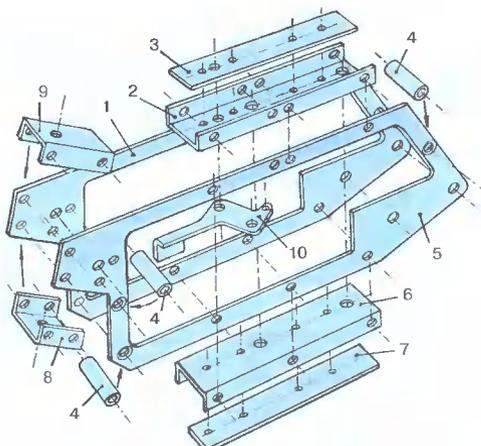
Детали рамы: 1 — правая боковина; 2 — верхняя деталь рамы; 3 — верхняя опорная планка; 4 — распорная втулка; 5 — левая боковина; 6 — нижняя деталь рамы; 7 — нижняя опорная планка; 8 — нижний кронштейн оси поворота; 9 — верхний кронштейн оси поворота; 10 — поворотный кронштейн ролика.
